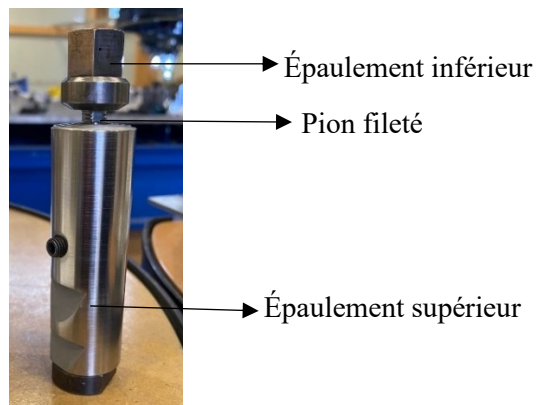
Pion à double épaulement utilisé pour le soudage
